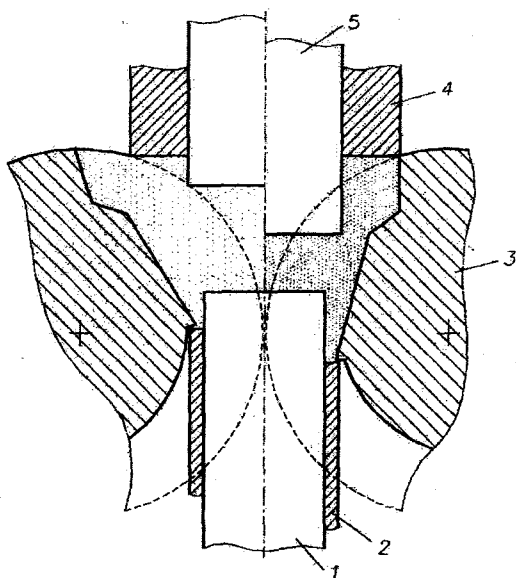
Формование порошковой заготовки в матрице, образованной вальцами
